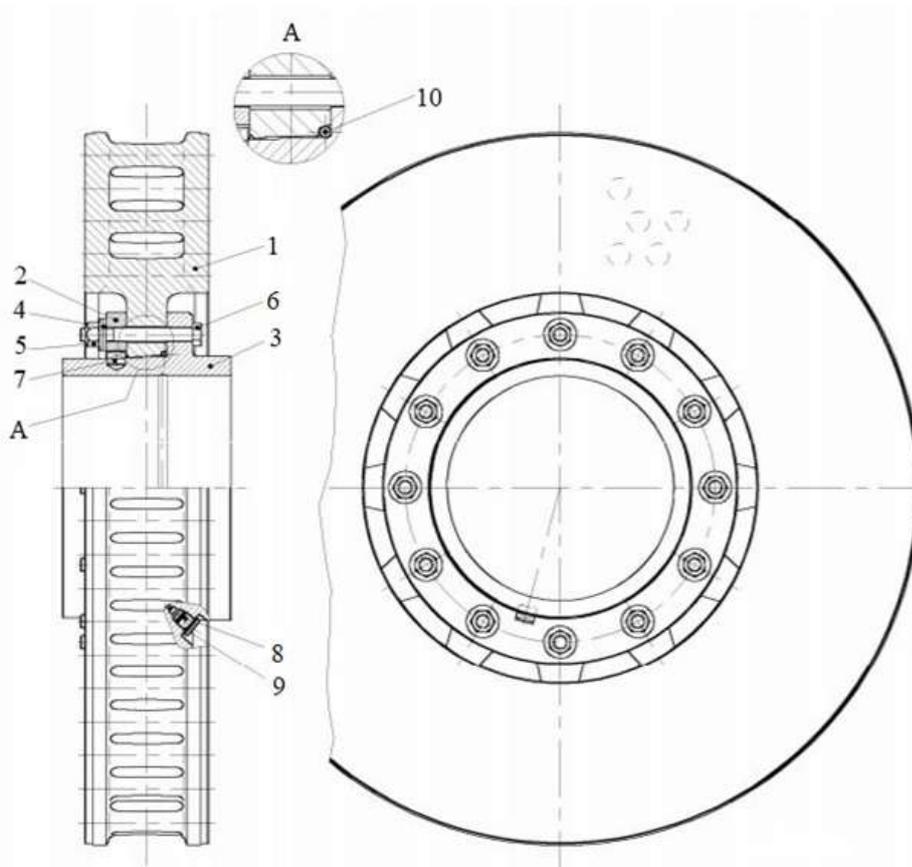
Осевой тормозной диск: 1-фрикционный диск; 2-зажимное кольцо; 3-ступица; 4-зажимная шайба; 5-стопорная гайка; 6-винт с шестигранной головкой; 7-болт для стопорения вращения; 8-резьбовая пробка; 9-уплотнительное кольцо; 10-центрирующее кольцо.
